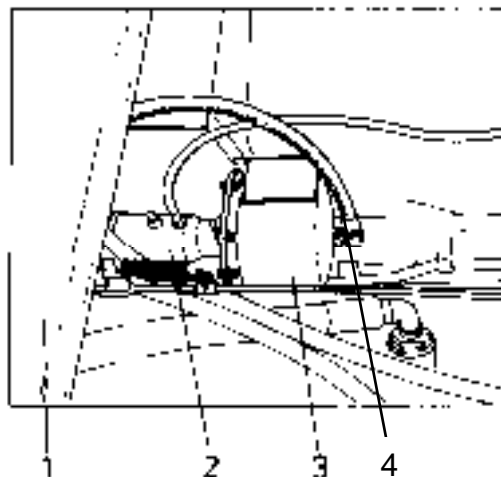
Расположение пневмоусилителя и главного тормозного цилиндра на задней раме (под кабиной). (Вид с левой стороны сверху)
